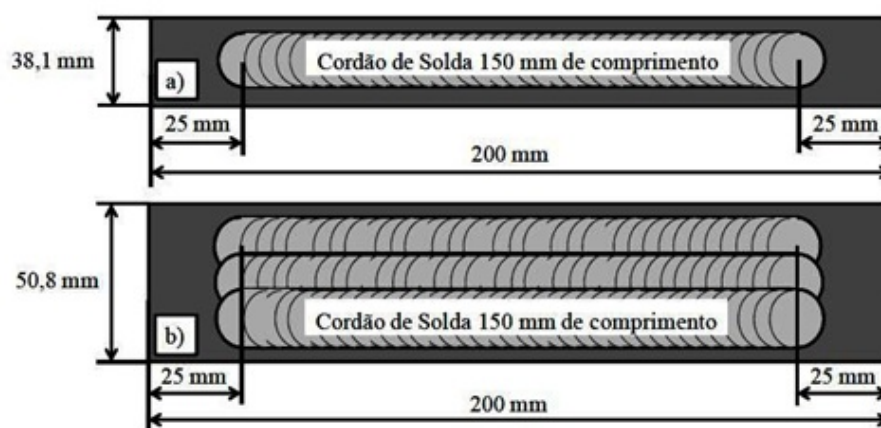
Esquema com as dimensões das chapas: a) representação da chapa que será utilizada para depositar um cordão de solda; b) representação da chapa que será utilizada para fazer o revestimento. Fonte: autoria própria.
